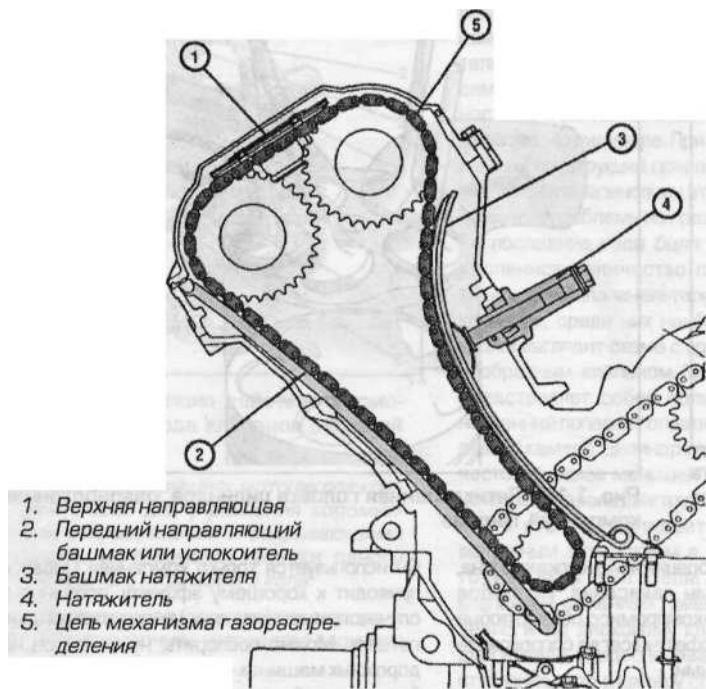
н Натяжитель и успокоитель цепи привода на двигателях с механизмом газораспределения DOHC
